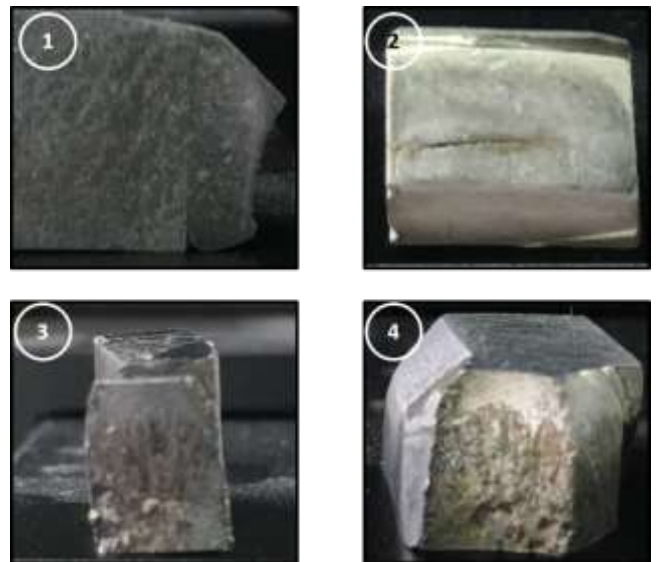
Diferentes probetas analizadas, 1) sección transversal del cordón de soldadura; 2) sección longitudinal del cordón de soldadura; 3) y 4) fractografía del cordón de soldadura.
